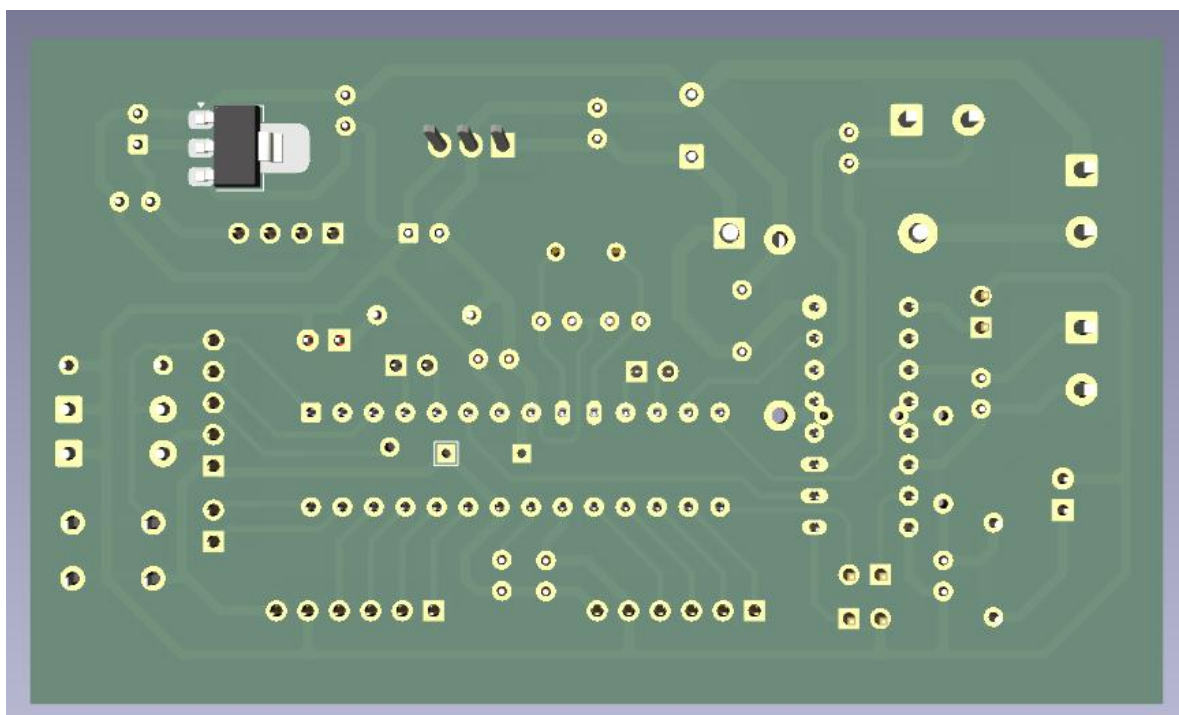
b: PCB Layout Mainboard (Highlight GND)
